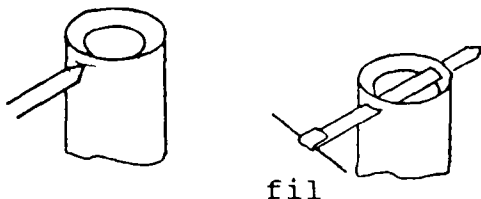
Percer les extrémités du tube en carton de façon que les pièces de contact touchent les extrémités des piles. Fixer les fils de cuivre sur les pièces de contact.
